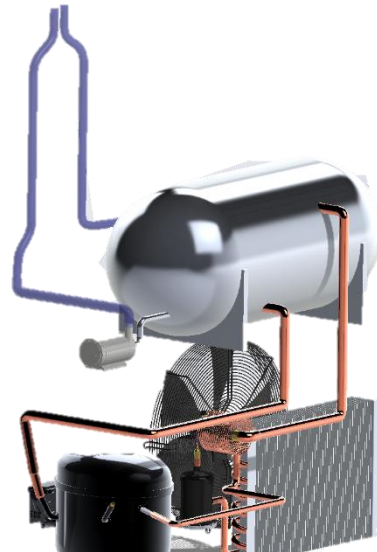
Vista isométrica del ensamblaje de los componentes del dispositivo
